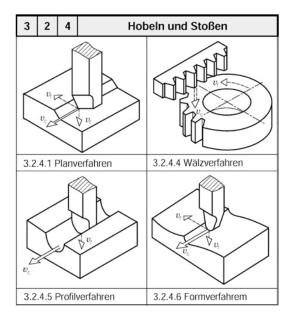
Plan-, Wälz-, Profil- und Formverfahren beim Hobeln und Stoßen / Rabotare plană, roţi dinţate, profilată [WES 10]
